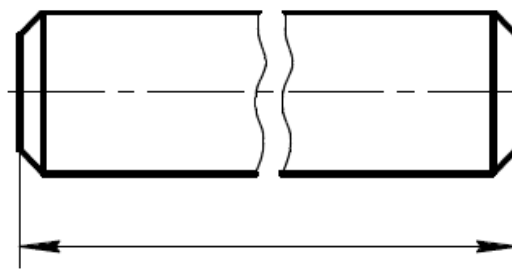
Нанесення розміру на кресленні деталі з розривом
